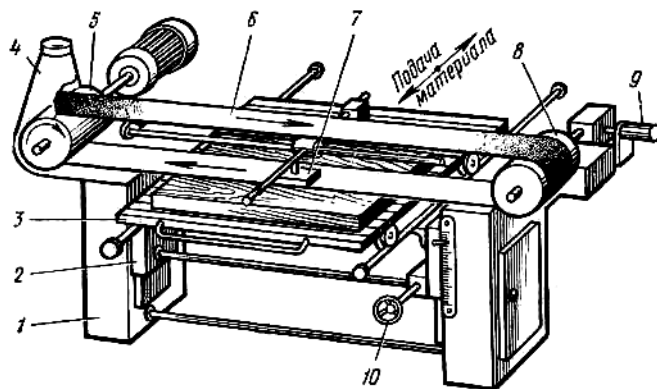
Ленточный шлифовальный станок с подвижным столом ШЛПС-5П: 1 — тумба, 2 — суппорт, 3 — стол, 4 — ограждение-пылеприёмник, 5 — приводной шкив, 6 — шлифовальная лента, 7 — утюжок, 8 — неприводной шкив, 9 — пневмоцилиндр, 10 — маховичок
